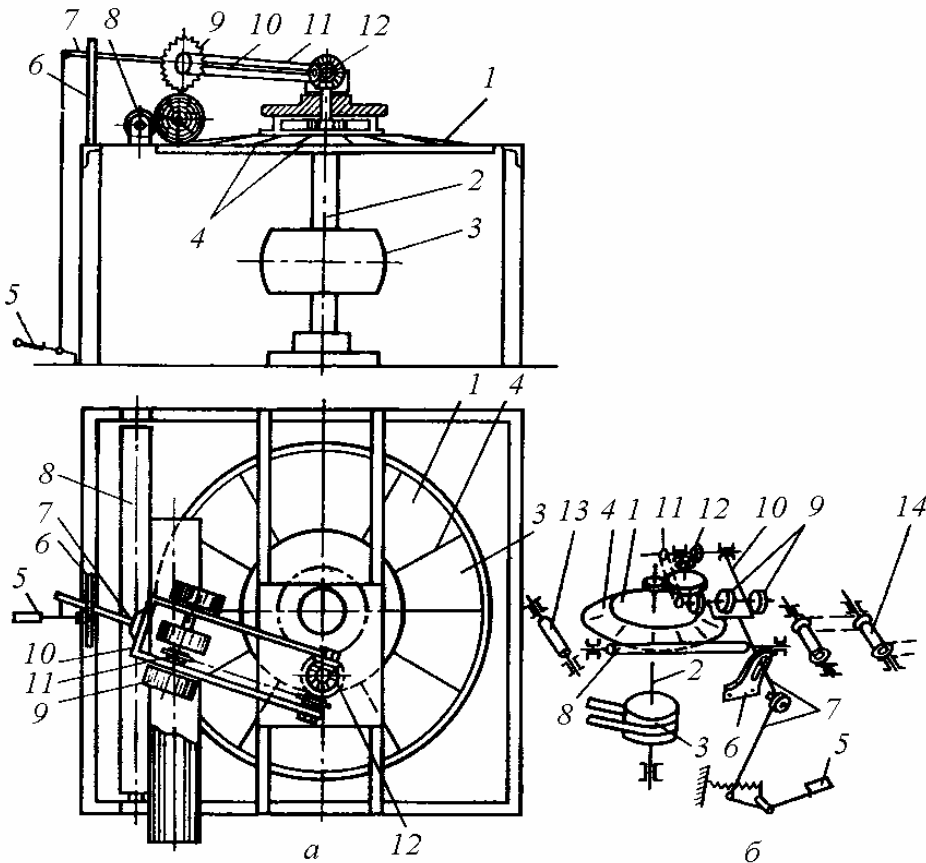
Дисковый окорочный станок ОД-1: *а* – схема общего вида; *б* – кинематическая схема; 1 – конический ножевой диск; 2 – вал диска; 3 – приводной шкив; 4 – ножи; 5 – педаль; 6 – направляющая рамка; 7 – рычаг; 8 – направляющий ролик; 9 – питающий валец; 10 – качающаяся рамка; 11 – цепная передача; 12 – коническая зубчатая передача; 13 – ролик приемного транспортера; 14 – подающий транспортер
